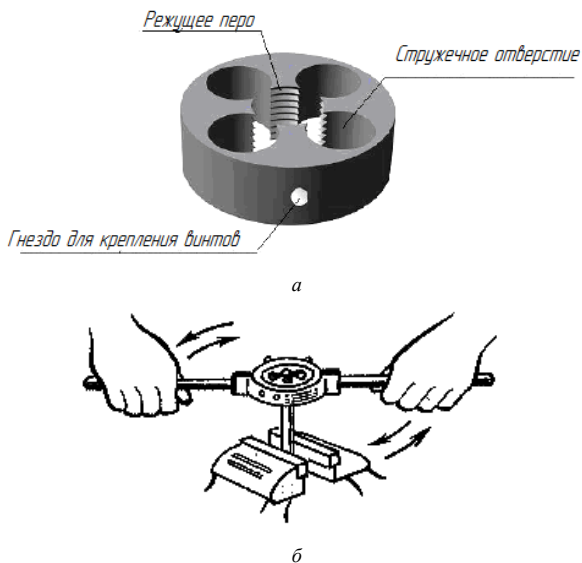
Обработка круглыми плашками: *а* – плашка; *б* – нарезание резьбы вручную с помощью плашкодержателя
